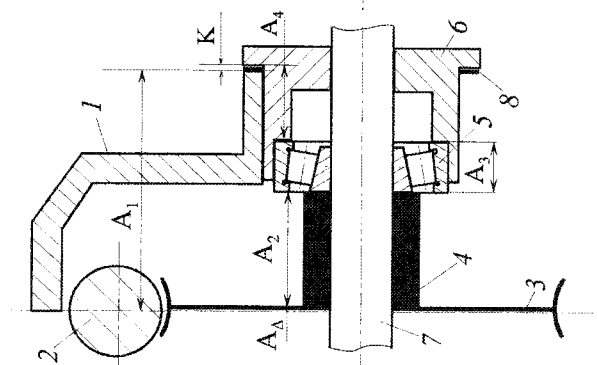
Эскиз редуктора после введения компенсатора в размерную цепь и схема размерной цепи: 1 — корпус редуктора; 2 — червяк; 3 — червячное колесо; 4 — ступица червячного колеса; 5 — подшипник качения; 6 — крышка подшипника качения; 7 — вал червячного колеса; 8 — компенсатор
